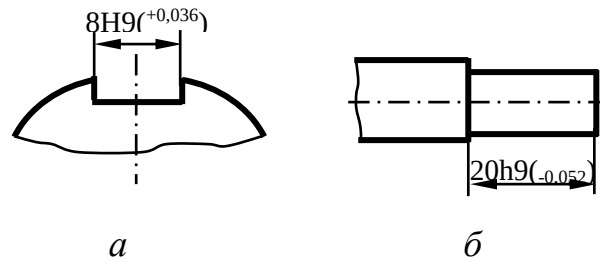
Випадки обов'язкової вказівки в кресленнях полів допусків разом із граничними відхиленнями
